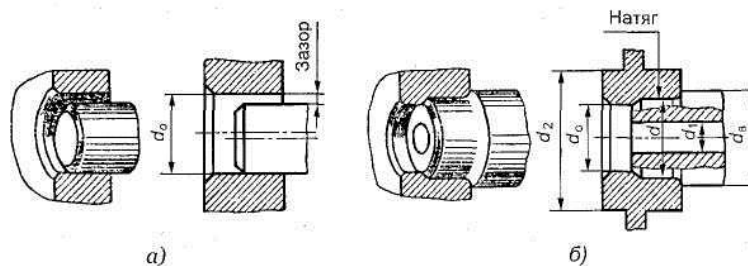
Соединения с гарантированным натягом: а — посадка с зазором; б — посадка с натягом
